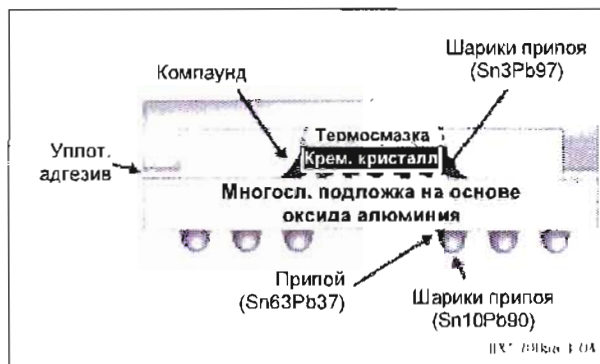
Керамический корпус BGA (CBGA) в разрезе
